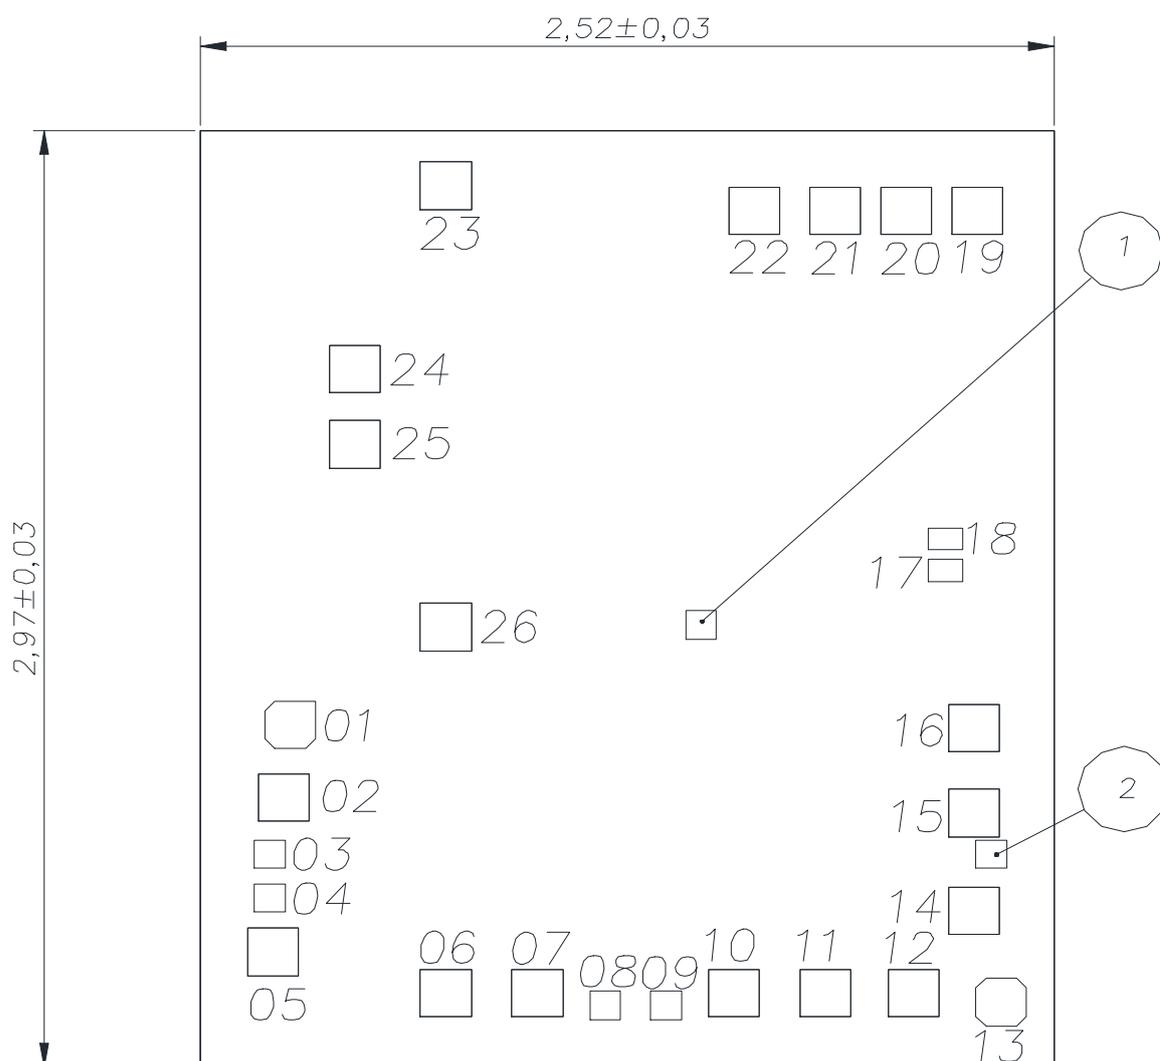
Габаритные размеры корпуса МК 5159.24-1
